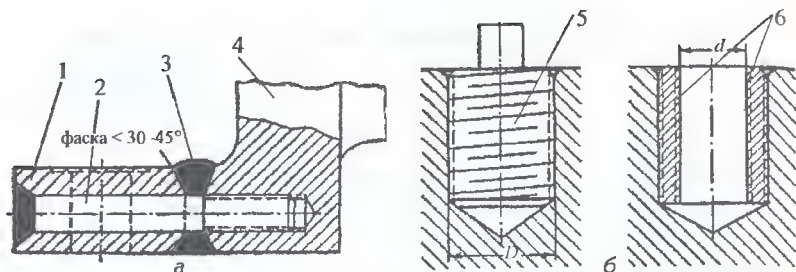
Приварка отколотой лапы у корпуса электрической машины (а) и ремонт резьбы в отверстиях станины (б): 1 — лапа; 2 — ввертыш; 3 — место сварки; 4 — корпус; 5 — пробка; 6 — новая резьба
